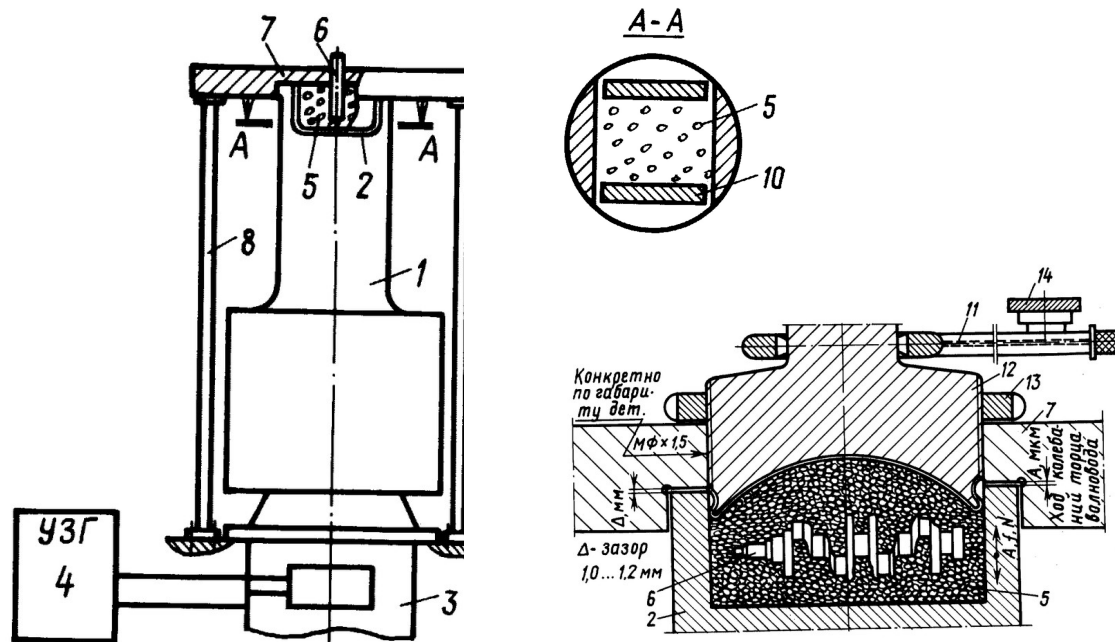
Пристрій для зміцнення деталей «коленвал»
